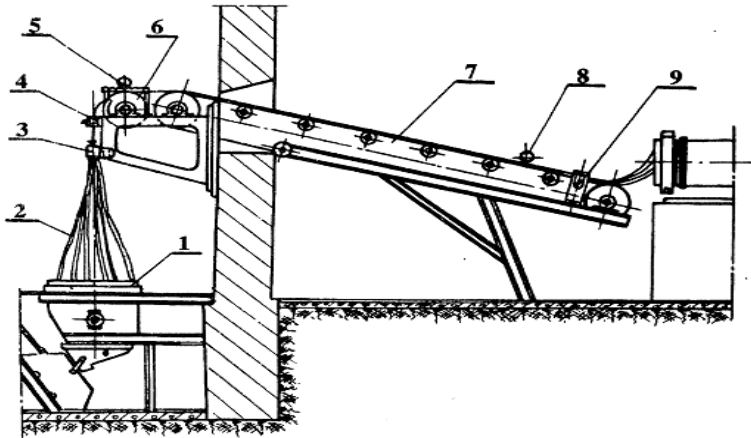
Безперервний агрегат для різання порохових шнурів: 1 – нижній різальний верстат; 2 – трубки; 3 – верхній різальний верстат; 4, 8 – притискний валик; 5 – ролик; 6 – барабан; 7 – похилий транспортер; 9 – гребінка
